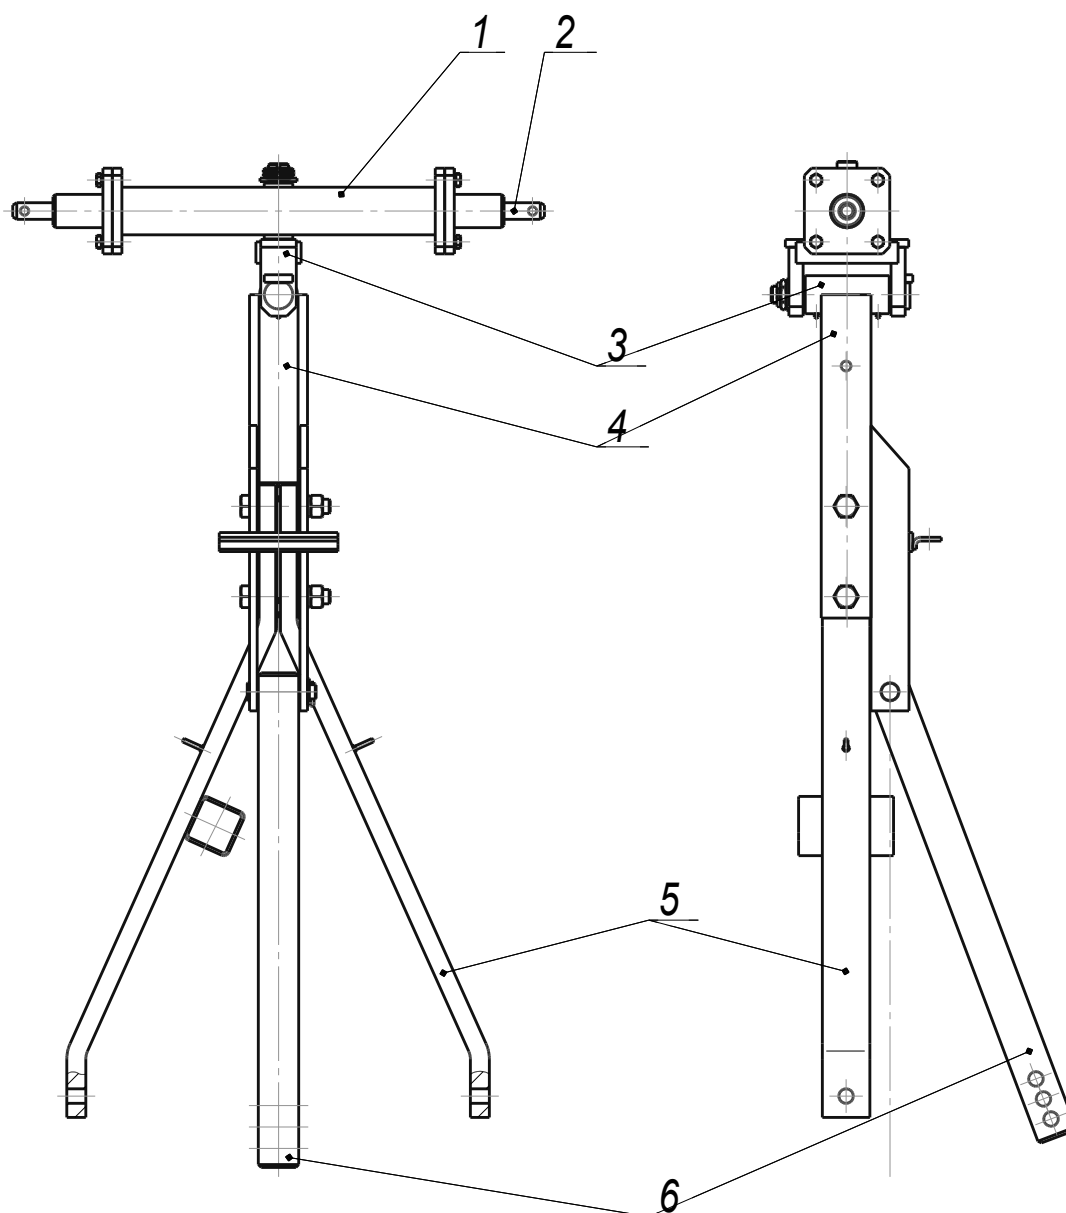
Причіпний пристрій культиватора КП-8,5
